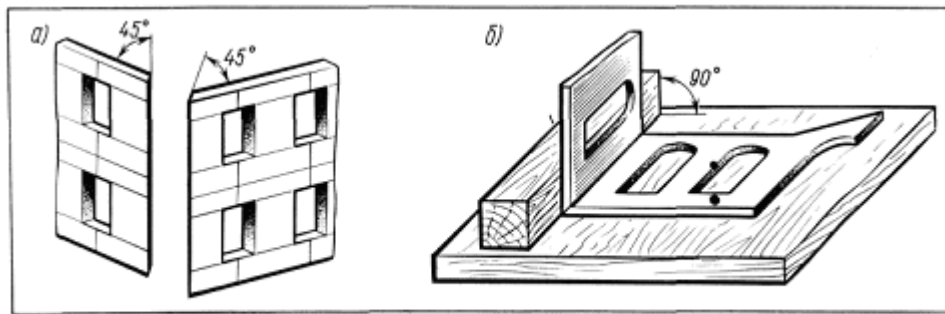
Соединение стен макета здания (а) и сборка каркаса здания на поверочной плите (б)
